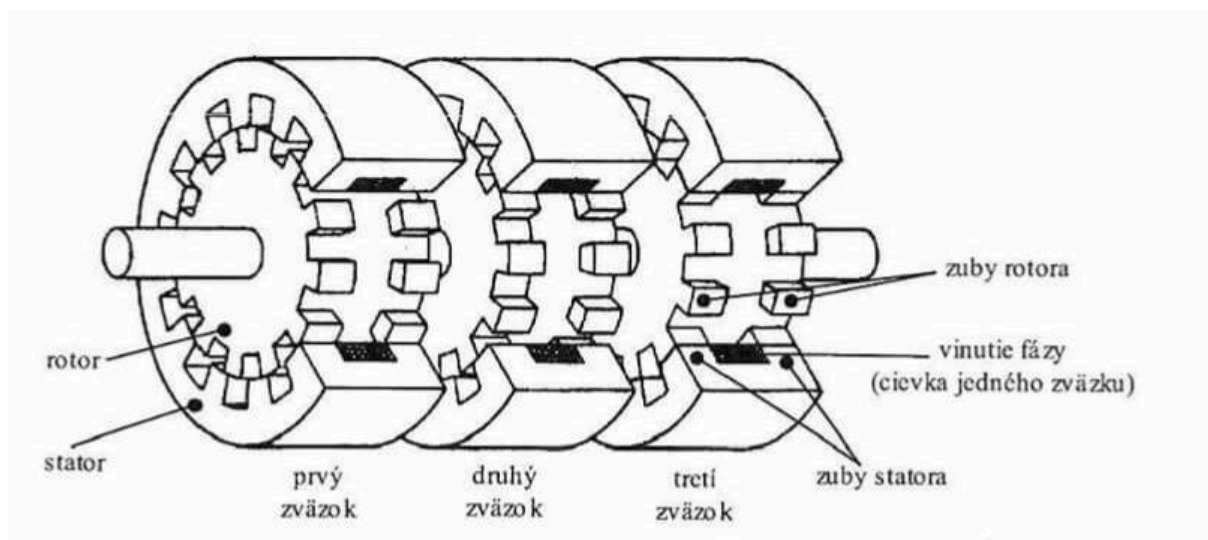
Průřez krokového motoru s proměnlivou reluktancí a úhlem kroku 6° (převzato z [2])
